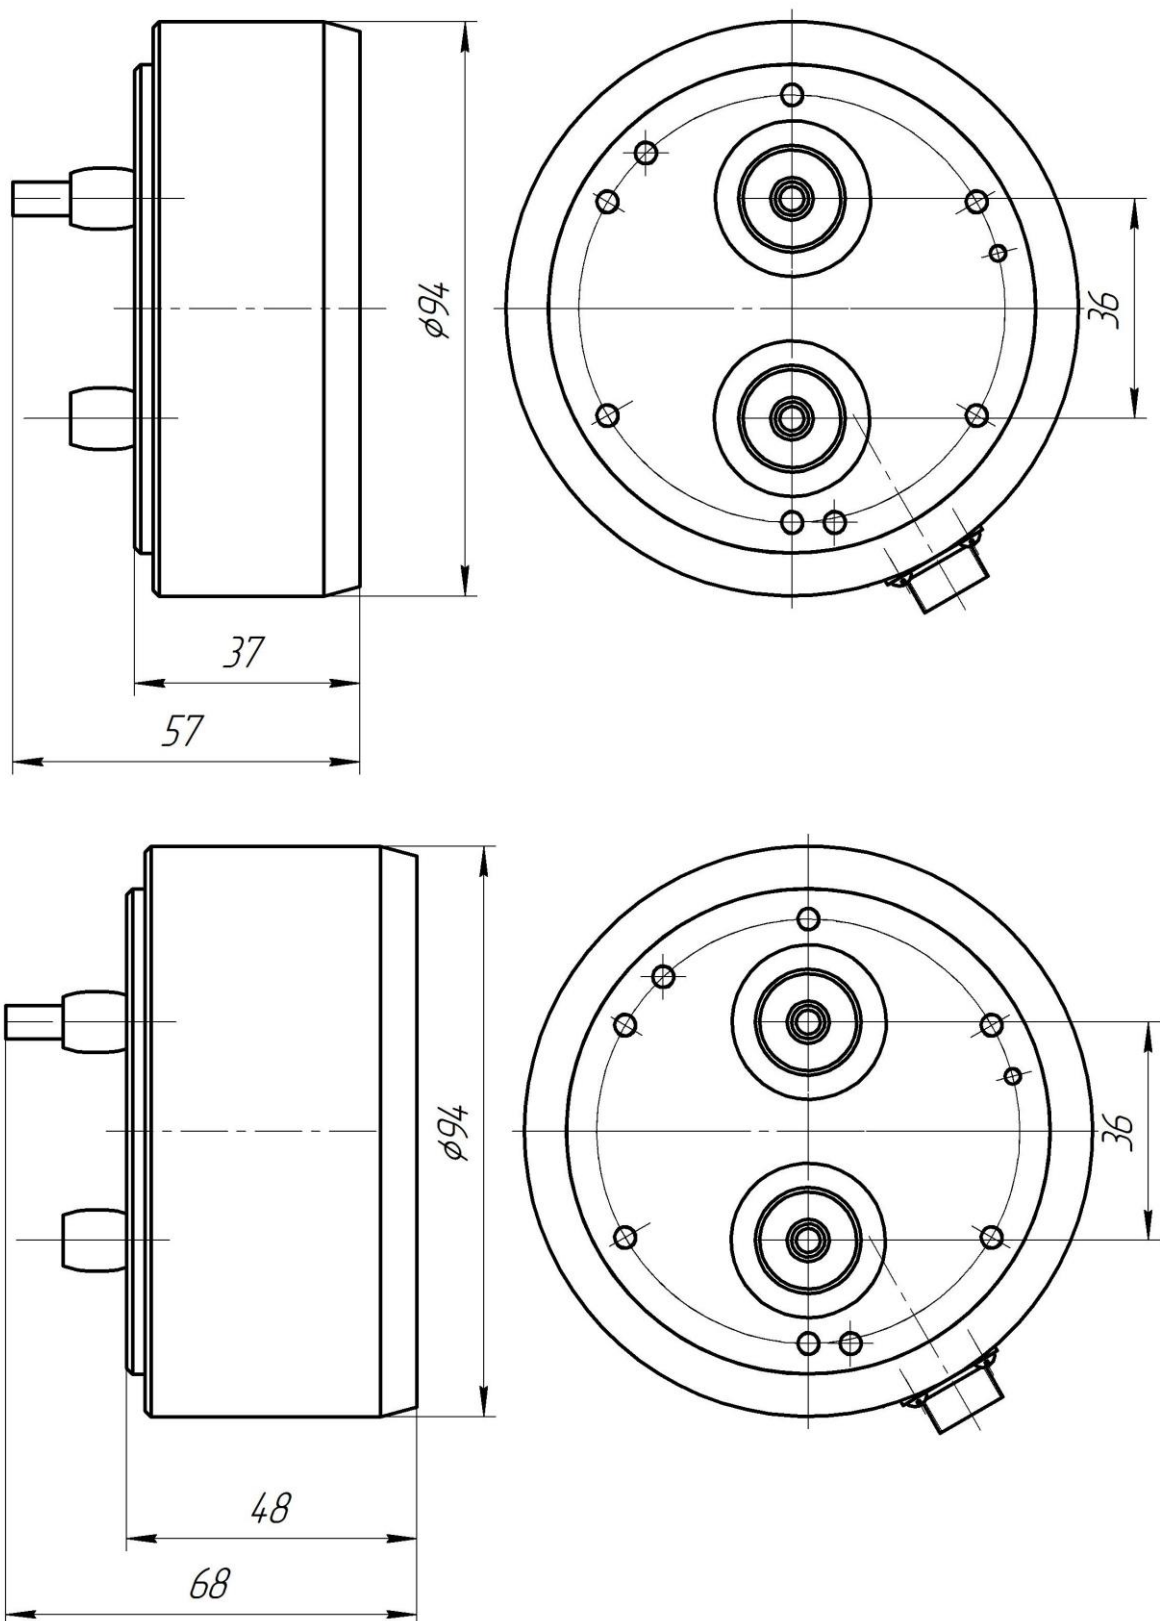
Габаритный чертеж блока датчиков ДК-1 (сверху); ДК-2 и ДК-3 – снизу.
